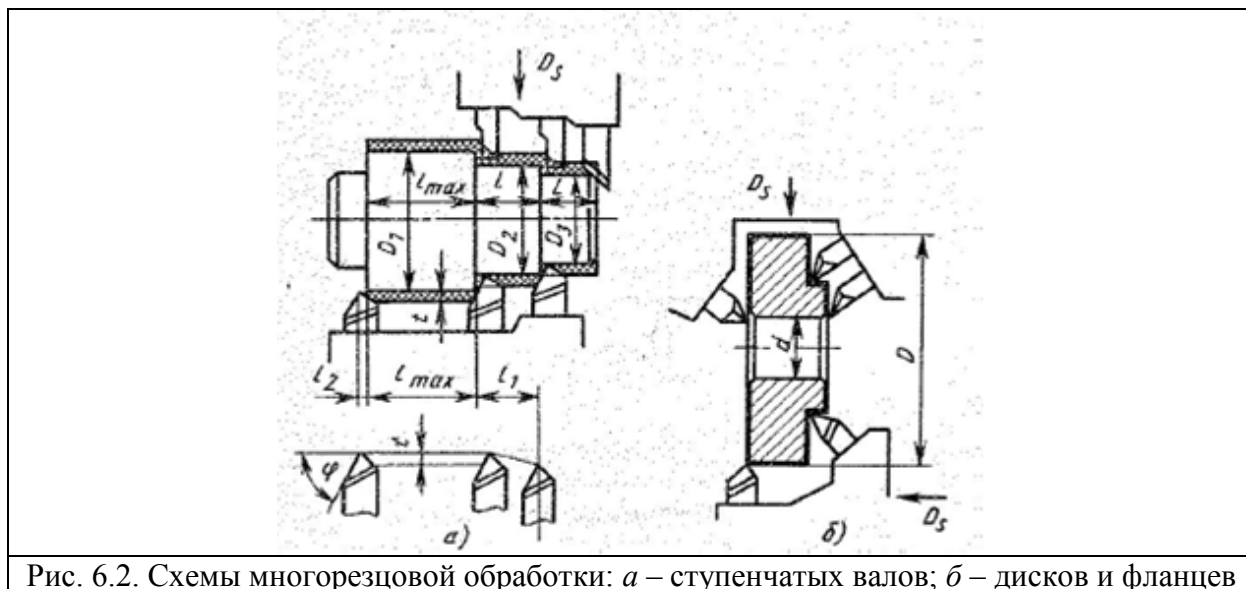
Схемы многорезцовой обработки: а – ступенчатых валов; б – дисков и фланцев
